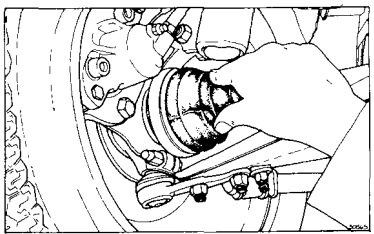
Проверка состояния чехла вала привода переднего колеса
